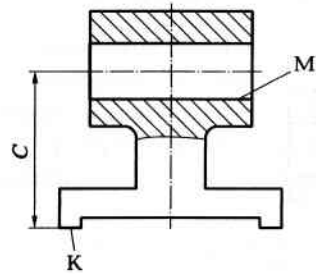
Эскиз обрабатываемой детали к заданию 1.32
